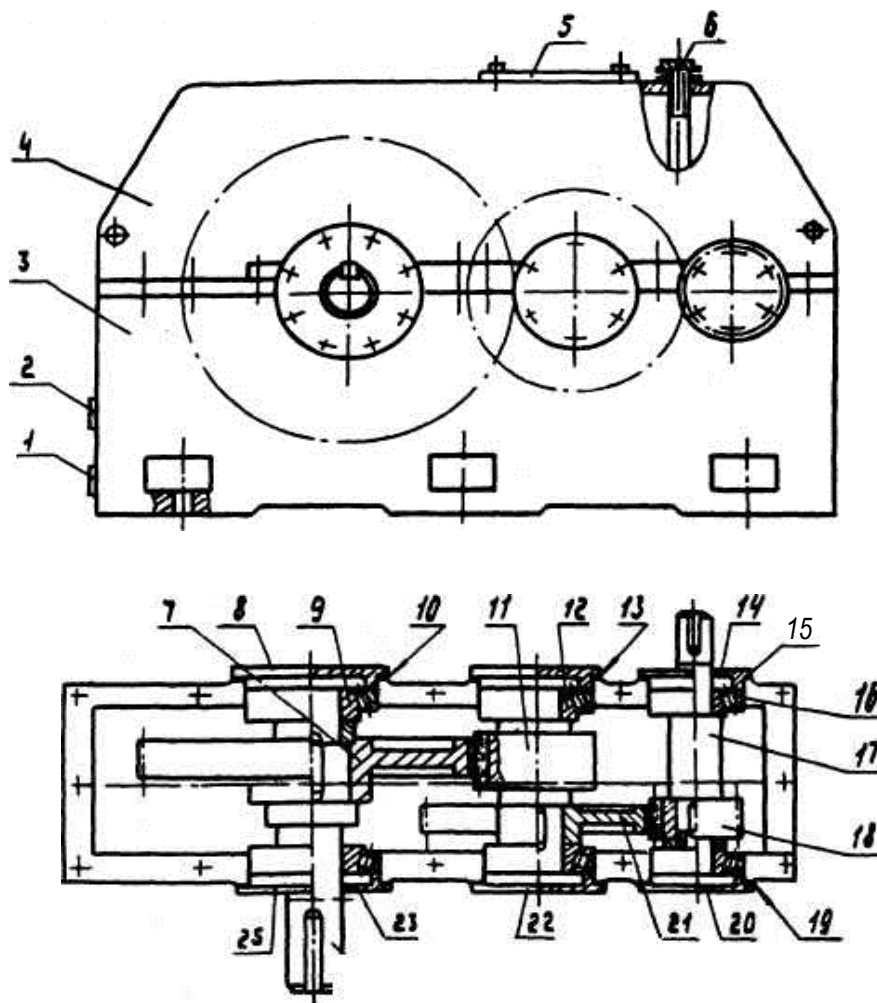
П7 Общий вид редукторов типа 1Ц2У
